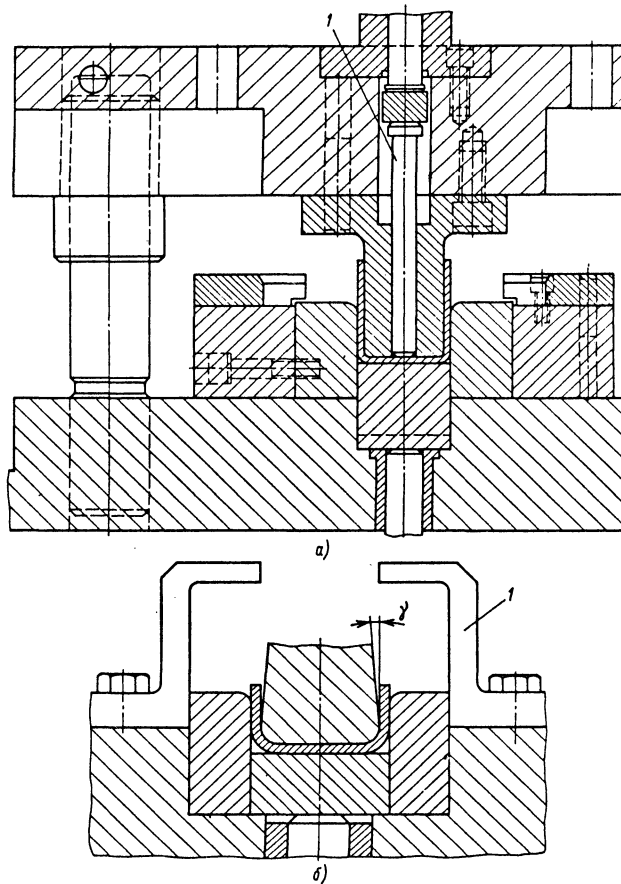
Типовые конструкции рабочих частей штампов для U-образной гибки
